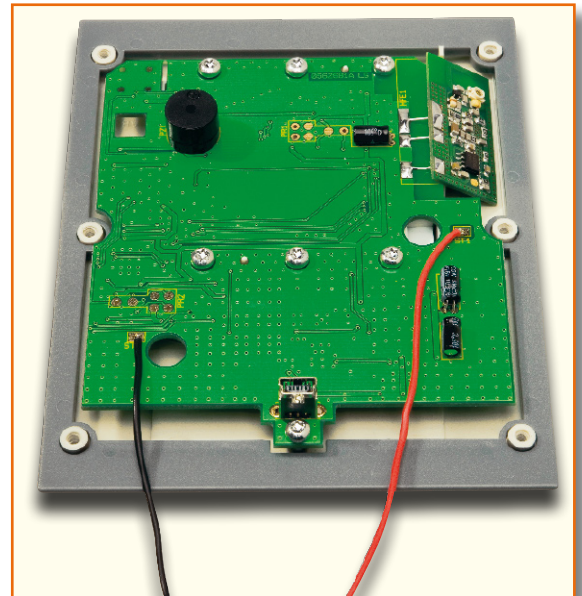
Detailansicht zum Anlöten der Batterie Anschlussleitungen
